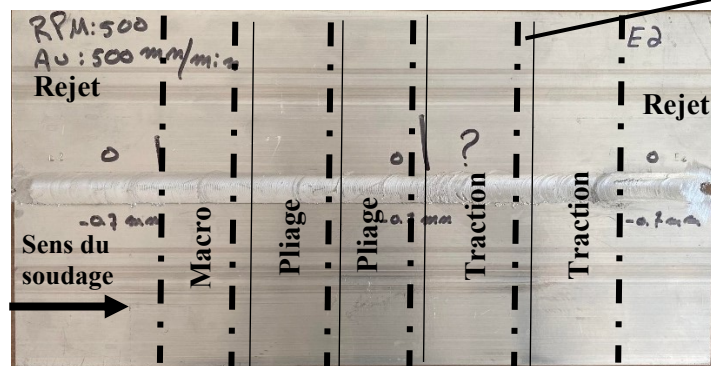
Illustration du plan d'usinage sur les extrusions soudées
